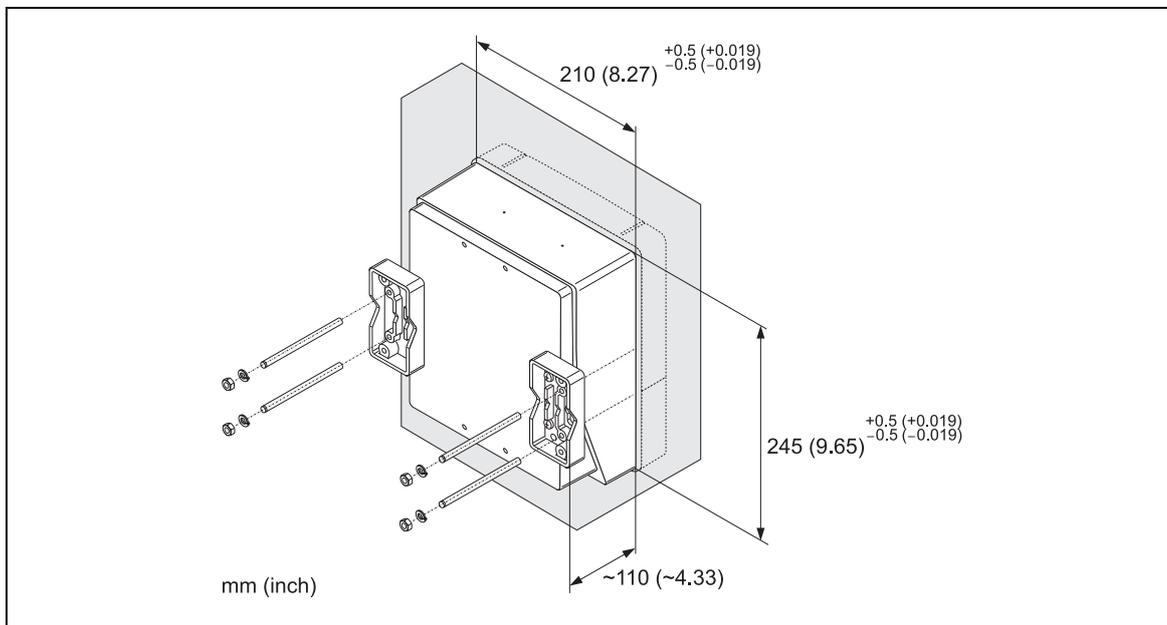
Монтаж на панели (корпус для монтажа на стену)
